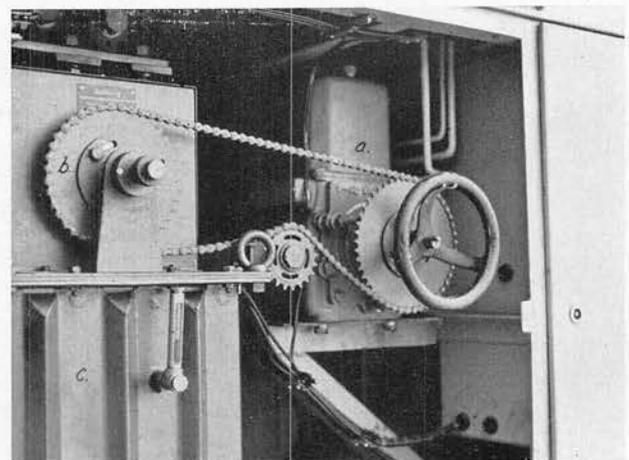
Ansicht einer elektro-hydraulischen Steuerung vom MS-Schweißgleichrichter
